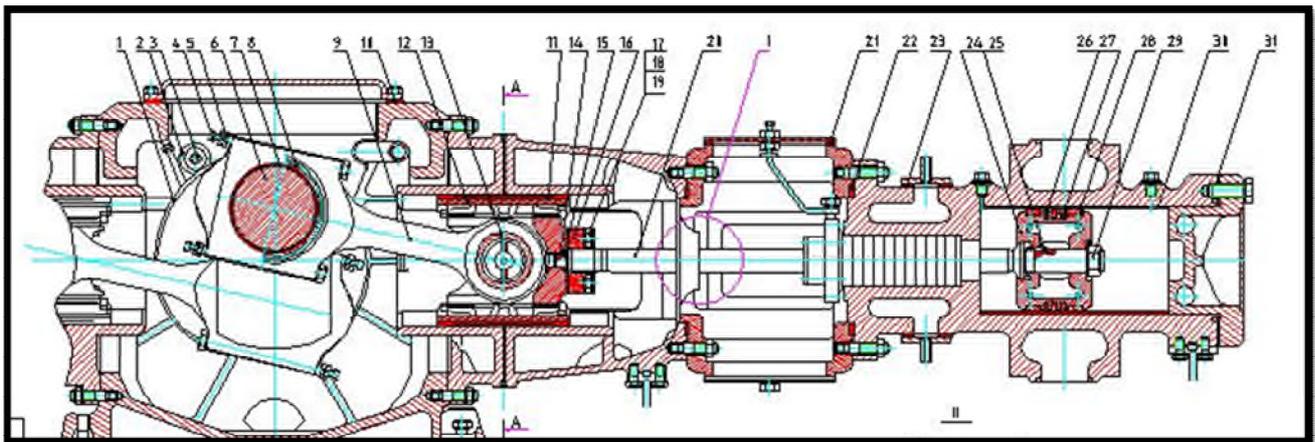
Esquema Conjunto de elementos que componen al compresor reciprocante
